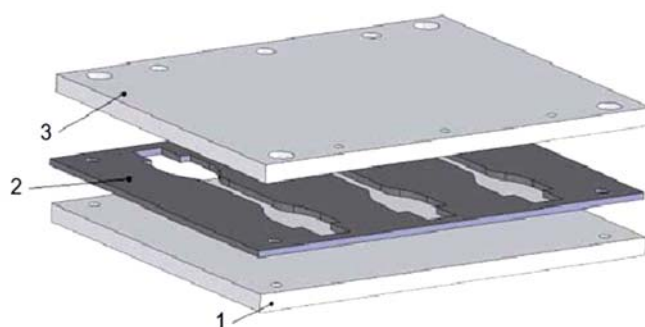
Molde utilizado no fabrico de provetes *bulk*: 1) placa inferior; 2) placa intermédia e 3) placa superior [34]
